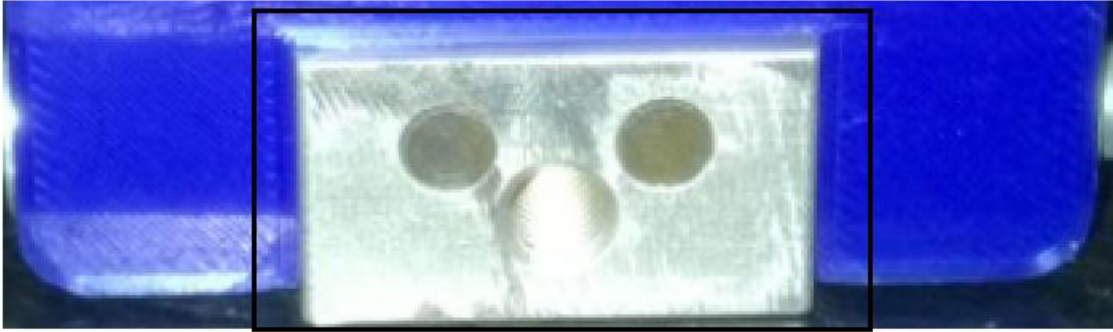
Ligação de encaixe entre “braçadeira” e caixa
